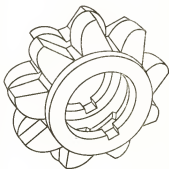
Долбяк для обработки зубчатой детали с невольвентным профилем
